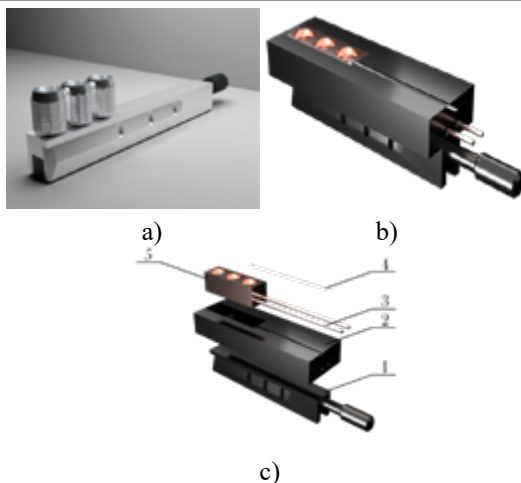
Трехмерная модель выдвижного держателя. а) стандартный выдвижной держатель образцов, б) модернизированный специализированный выдвижной держатель образцов в собранном виде, в) модернизированный специализированный выдвижной держатель образцов в разобранном виде. 1 – ручка держателя, 2 – теплоизолирующая крышка держателя, 3 – криогенно-капиллярная система, 4 – датчик температуры (термопара), 5 – контейнер
